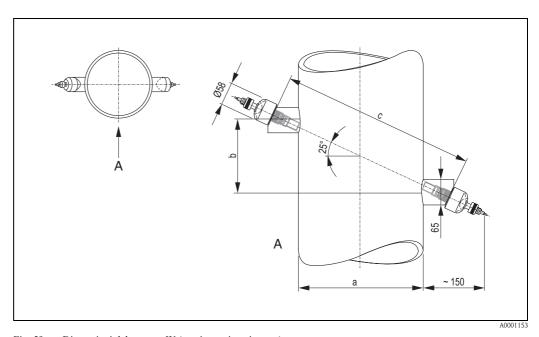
Dimensioni del sensore W (versione a inserimento)
